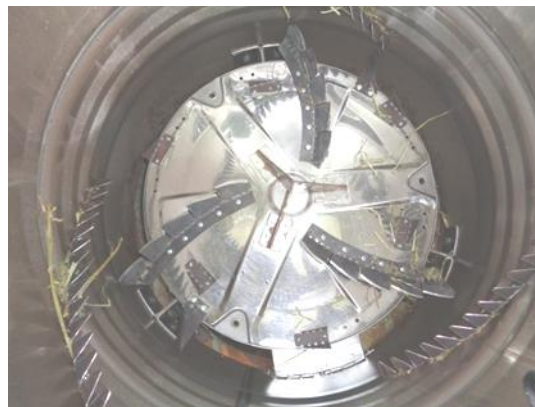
Дисковый рабочий орган, с комбинированными режущими сегментами
